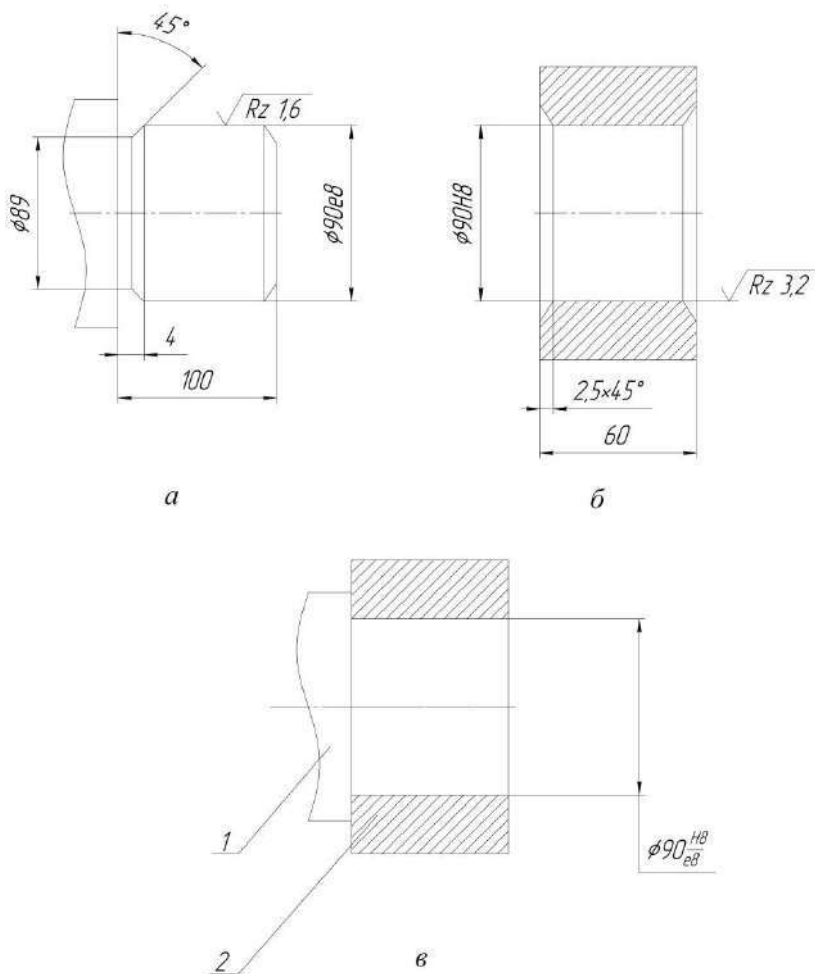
Эскизы: *a* – вала; *б* – втулки; *в* – сборочного чертежа соединения: 1 – вал; 2 – втулка
